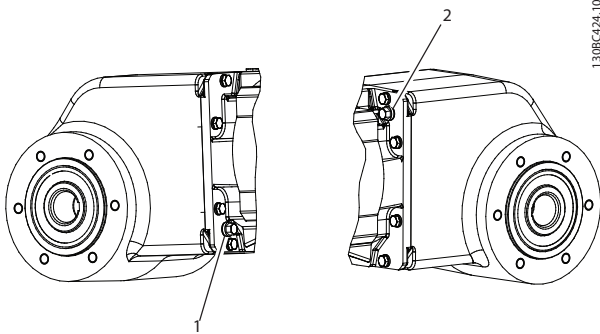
VLT® OneGearDrive Ölschrauben 1 und 2
